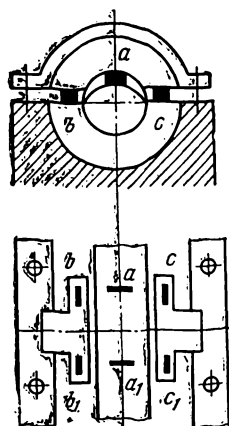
Измерение зазоров между шейкой вала и вкладышем подшипника скольжения
